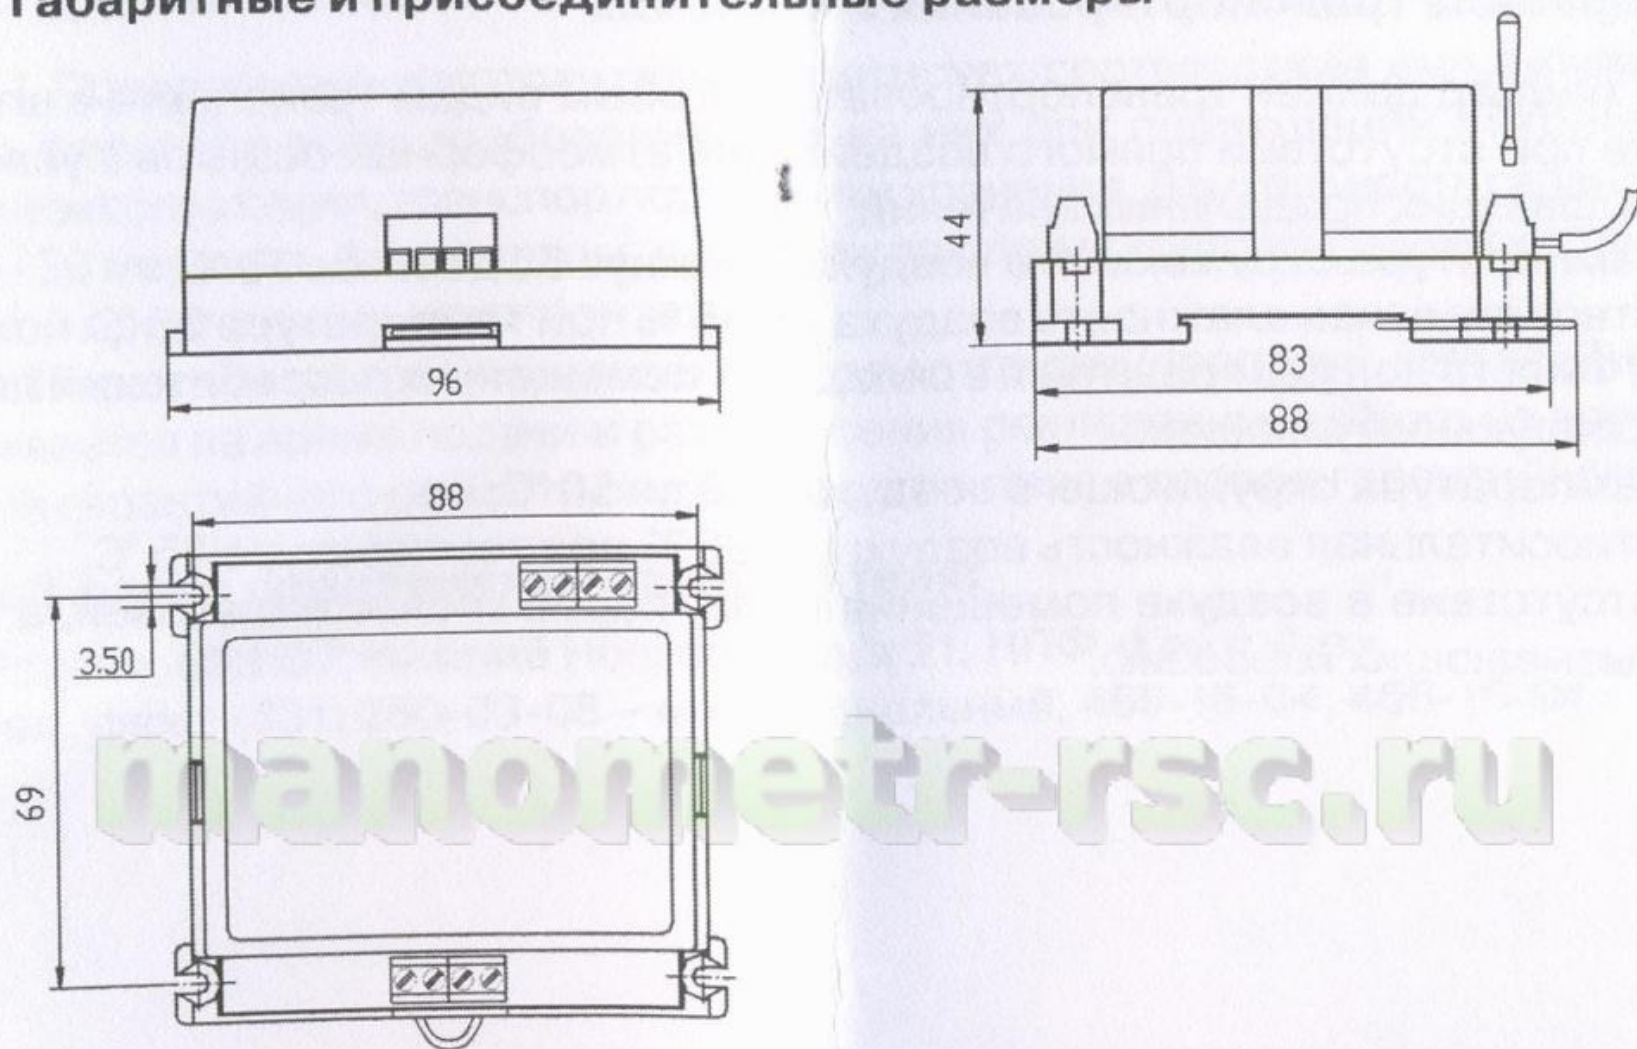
Габаритные и присоединительные размеры фильтра
